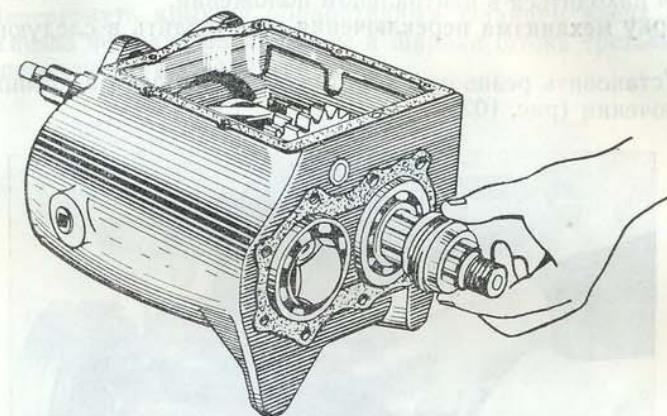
Установка шестерни привода спидометра и прокладки крышки задних подшипников коробки передач автомобиля УАЗ-451М
